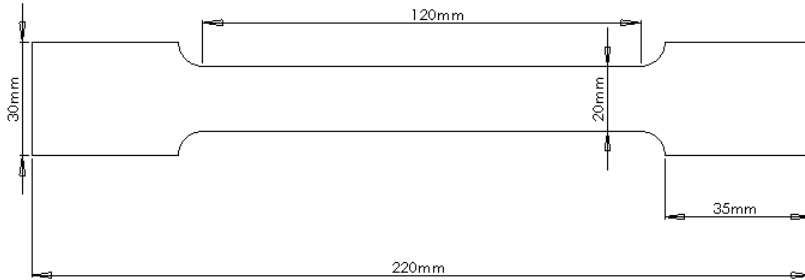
Dimensões do corpo de prova do ensaio de tração para a viga de aço.
